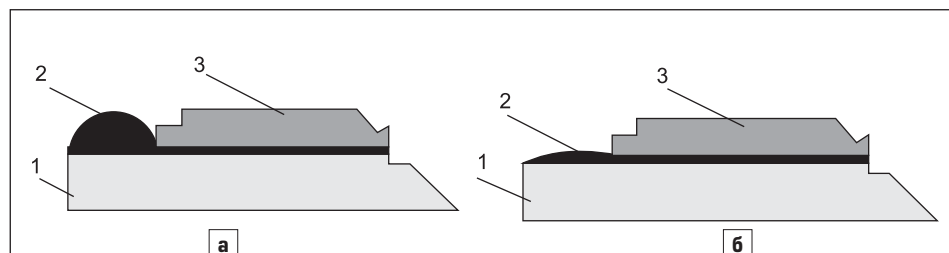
Форма паяного шва: а) с прижатием крышки; б) без прижатия в процессе герметизации (1 — основание корпуса; 2 — галтель припоя; 3 — крышка)
